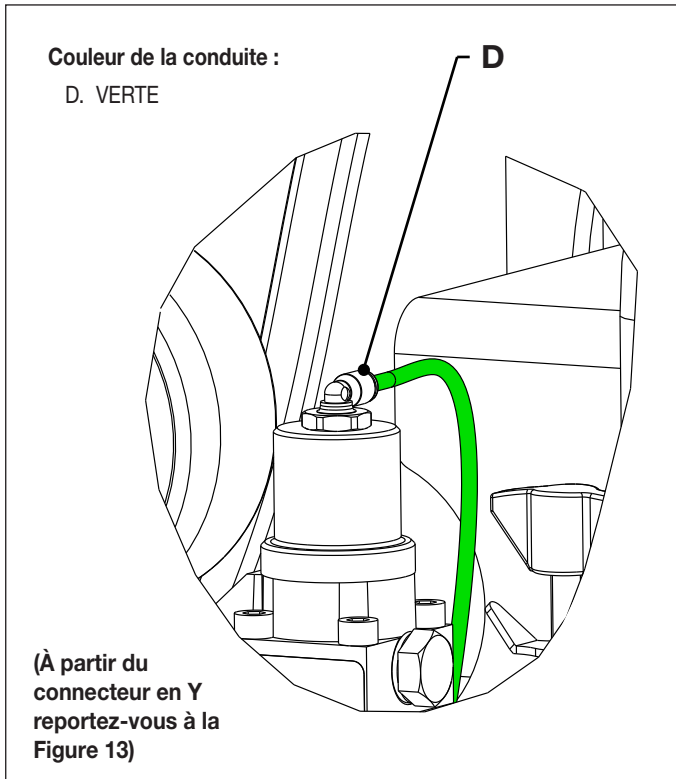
Raccordement de la conduite d'air - Distributeur hydraulique
